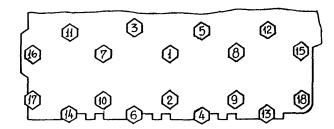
Порядок затяжки гаек головки цилиндров пригателя ЗМЗ-63-07
